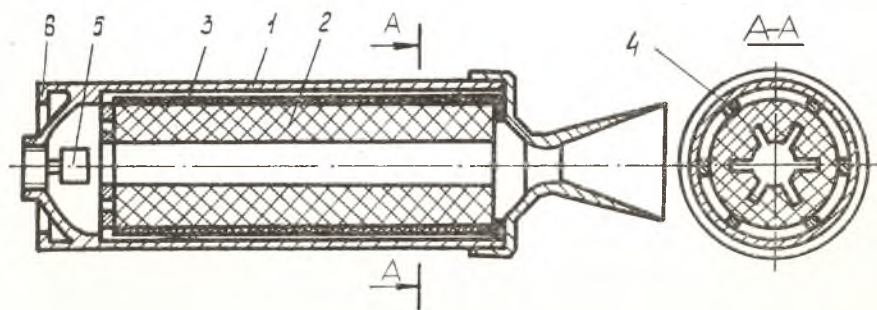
Схема РДТТ с вкладным зарядом: 1 — корпус; 2 — заряд; 3 — бронировка; 4 — вкладыш; 5 — воспламенитель; 6 — узел стыковки
